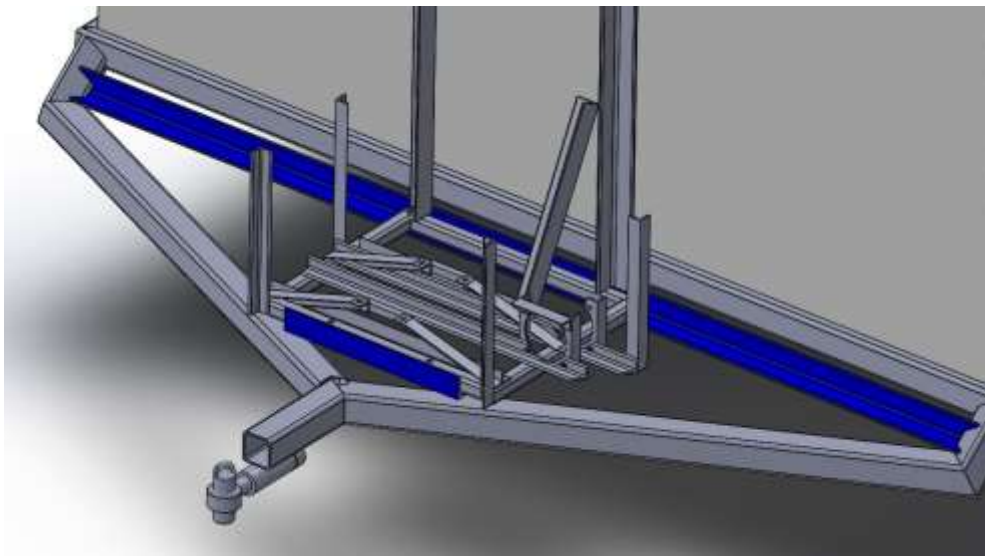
Cantoneiras soldadas ao chassi do reboque
